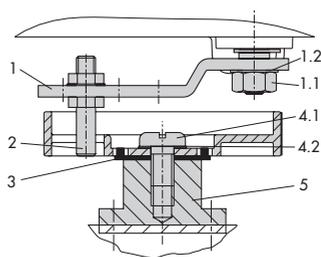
Montaje de la rueda de acoplamiento en el Tipo 3278
